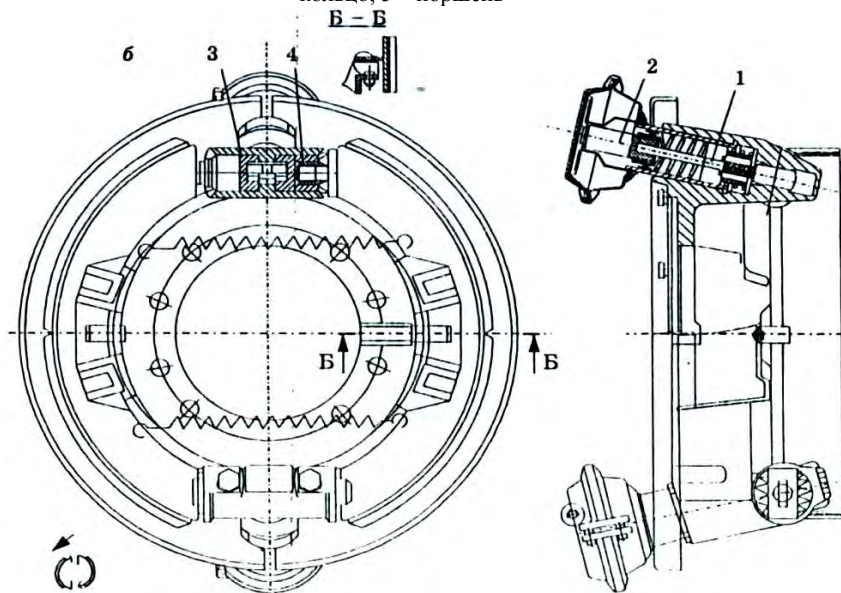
Схема барабанных тормозов с самоустанавливающимися колодками с разнесёнными опорными поверхностями:
